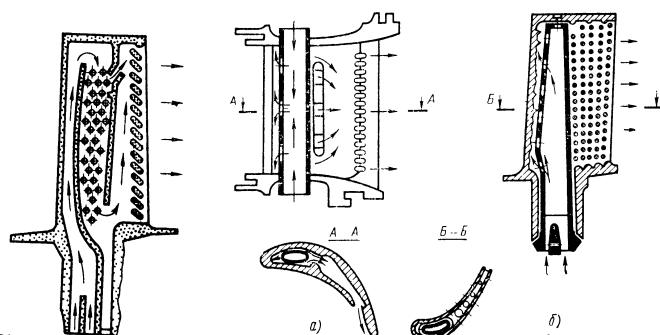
Слева - конструктивная схема рабочей лопатки со смешанным продольно-поперечным направлением движения охлаждающего воздуха и петлевым движением в продольном направлении (вторая ступень двигателя JT9D); справа - конструктивные схемы турбинных лопаток с дефлекторными вставками (а - сопловая лопатка первой ступени турбины двигателя «Конуэй»; б - рабочая первой ступени - JT9D-7)
